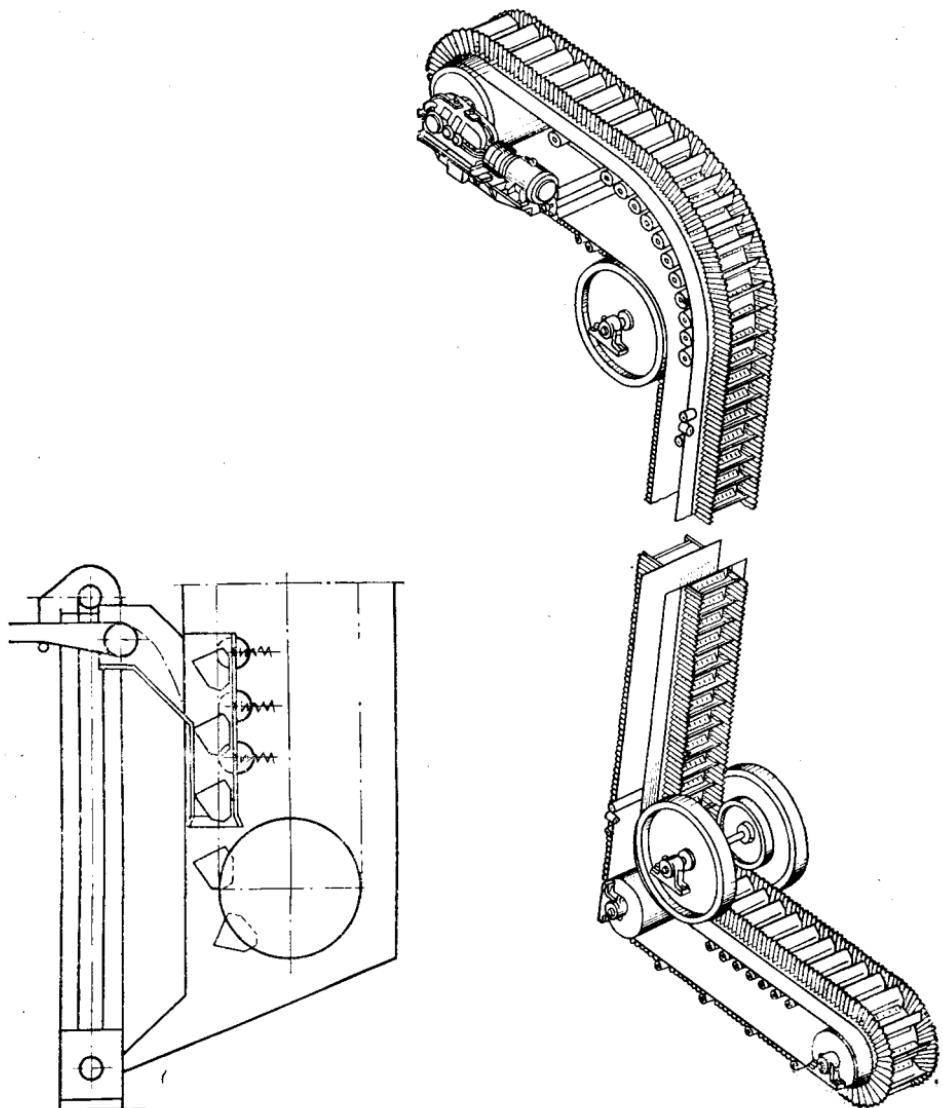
Погрузочное устройство шахтного ковшового элеватора
